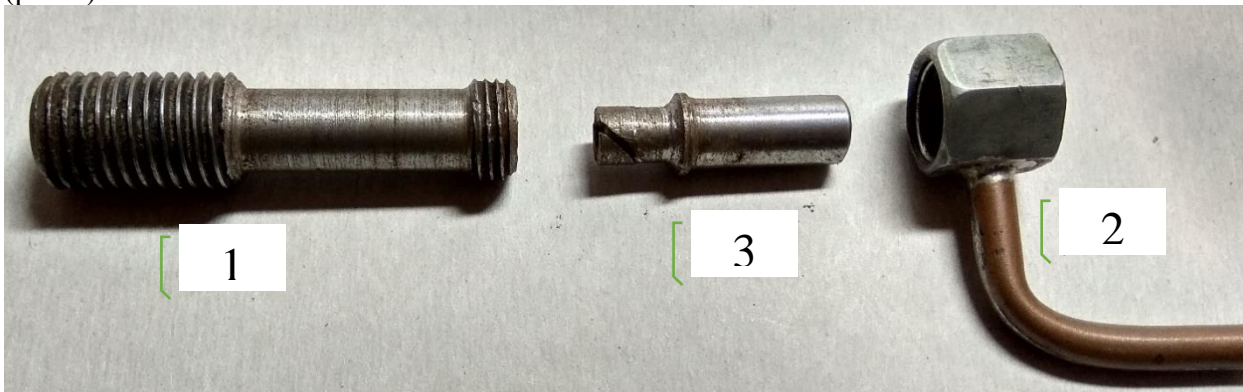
Форсунка пескоструйного аппарата: 1 - пневмо-вихревая насадка; 2 - гайка подвода воздуха; 3 - сопло
